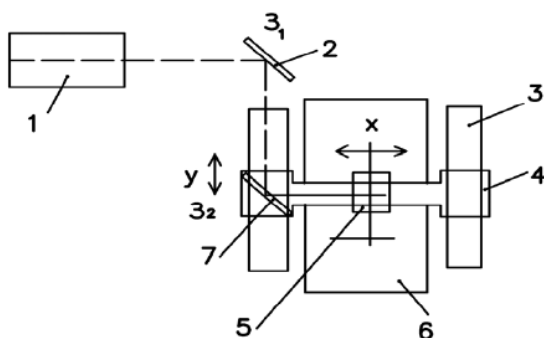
Схема порталной установки для лазерного раскроя листа: 1 - СО лазер; 2 - неподвижное зеркало Z_1 ; 3 - направляющие портала; 4 - портал, перемещающийся по направляющим (ось Y); 5 - каретка с зеркалом Z_2 и оптическим резаком, перемещающаяся по portalу (ось X); 6 - неподвижный стол для размерной обработки детали; 7 - подвижное зеркало Z_2 , укрепленное на портале
